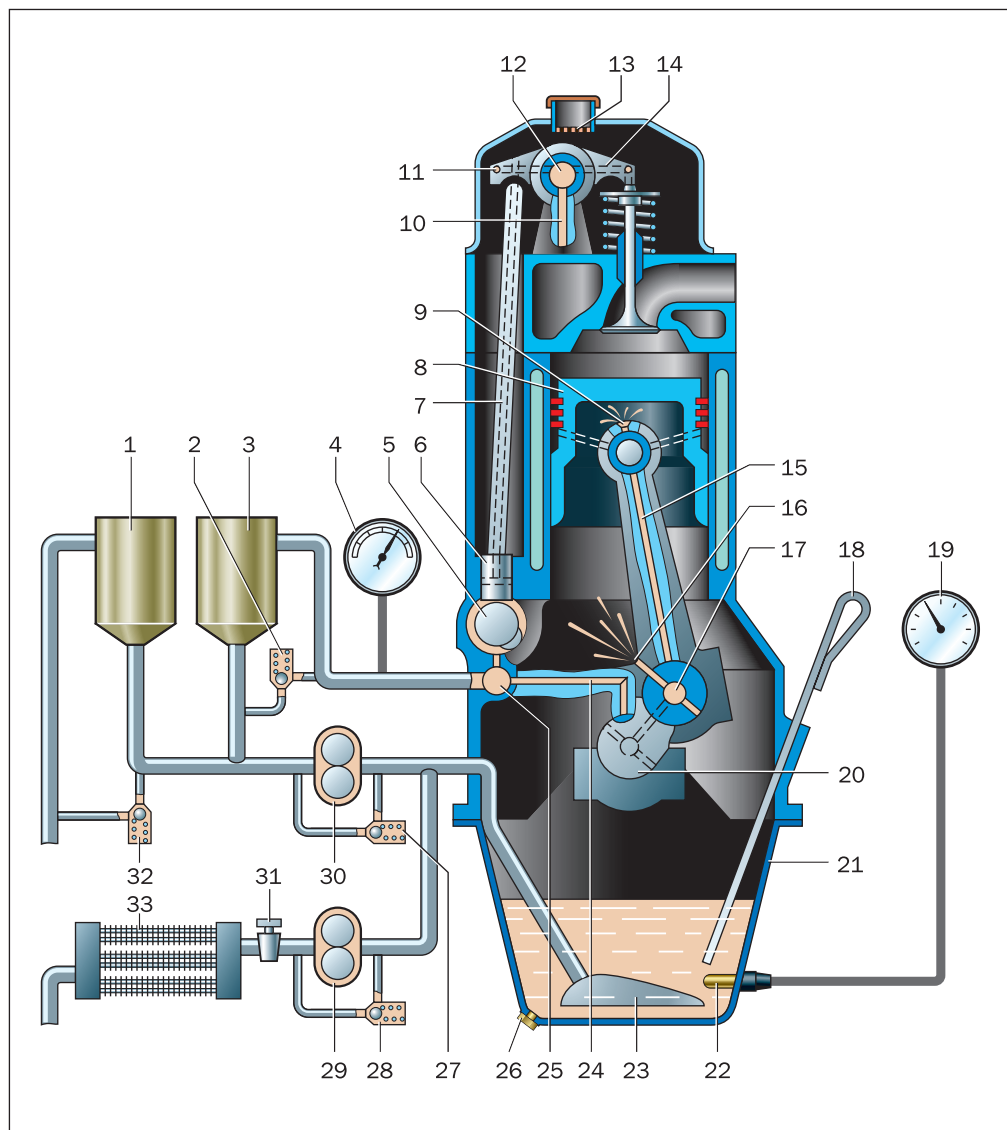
Принципиальная схема смазочной системы: 1,3 — фильтрующие элементы; 2, 27, 28, 32 — перепускные клапаны; 4 — манометр; 5 — распределительный вал; 6 — толкатель; 7 — штанга; 8 — поршень; 9 — распылитель; 10, 24 — сверление в блоке; 11, 14 — сверление в коромысле; 12 — полость оси коромысел; 13 — сетчатый фильтр; 15 — сверление в шатуне; 16 — распылитель в нижней головке шатуна; 17 — сверление в шейках коленчатого вала; 18 — щуп; 19 — термометр; 20 — коренной подшипник; 21 — поддон; 22 — температурный датчик; 23 — маслозаборник; 25 — главная масляная магистраль; 26 — сливная пробка; 29, 30 — масляный насос; 31 — кран; 33 — масляный радиатор
